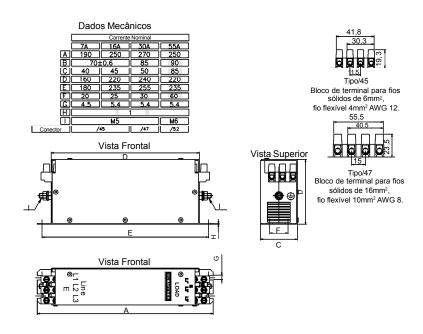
Desenho do filtro externo FS3258-xx-xx
